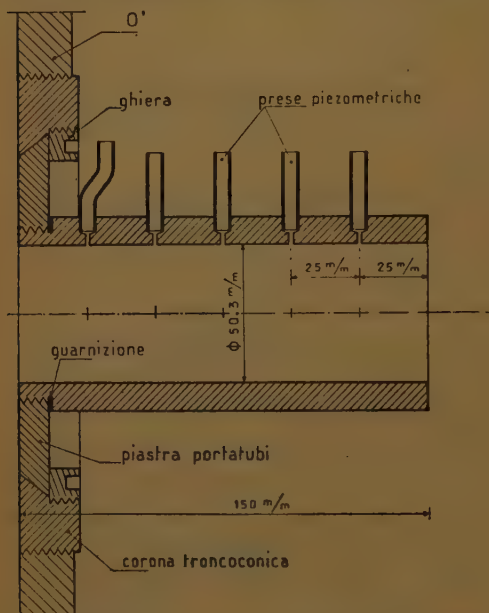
Sezione longitudinale di un tubo addizionale e posizione delle prese piezometriche alla parete.
